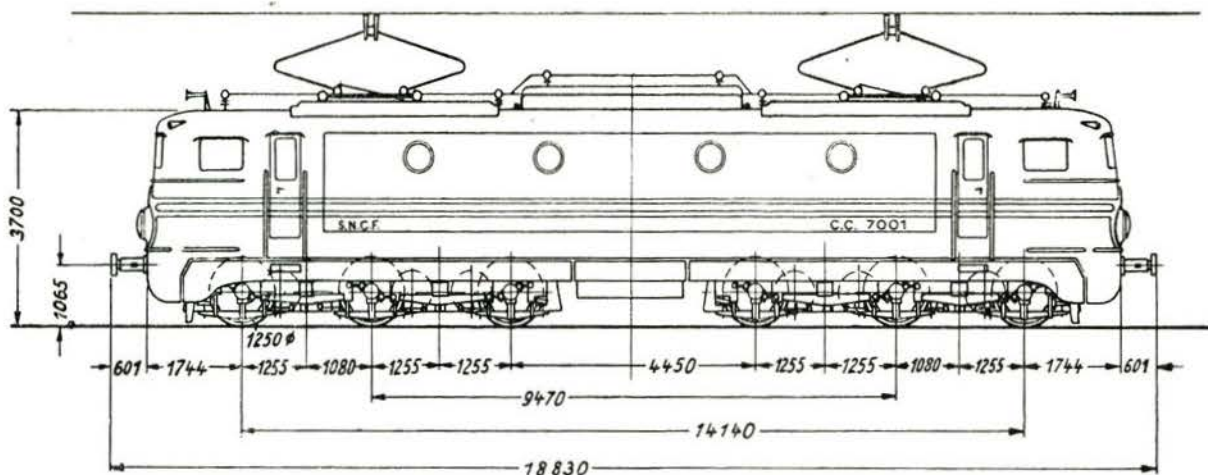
Typenskizze der Schnellzuglok, Serie C.C.-7000, Achsfolge Co'Co'
